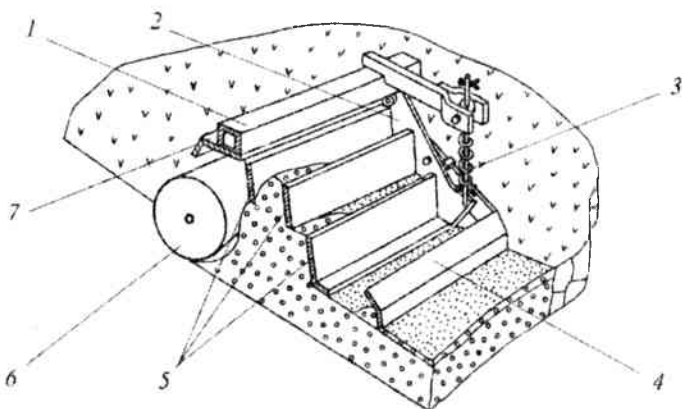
Почвообрабатывающая машина с жалюзиобразным кожухом:
